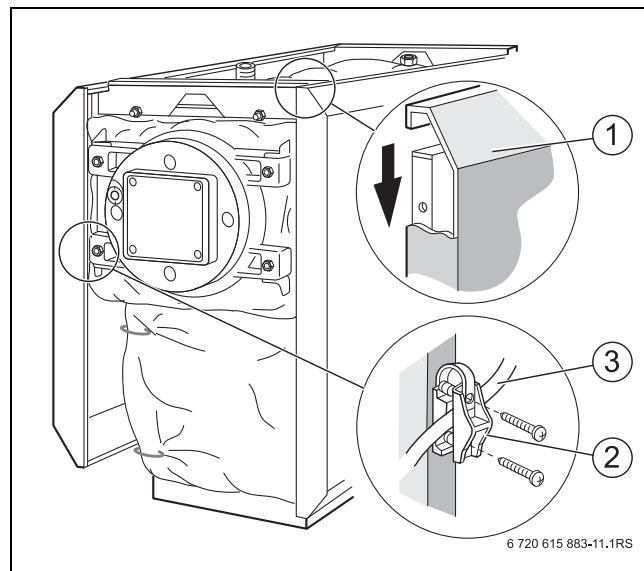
Encaixar os painéis laterais e colocar o cabo do queimador
